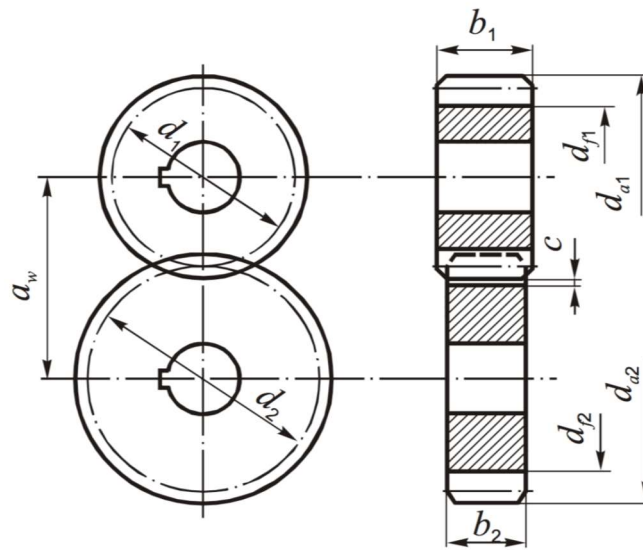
Схема прямозубої циліндричної передачі
